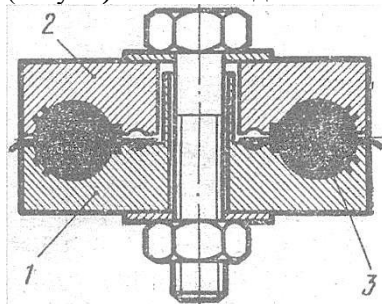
Пресс – форма для вулканизации колёс и сырой резины
